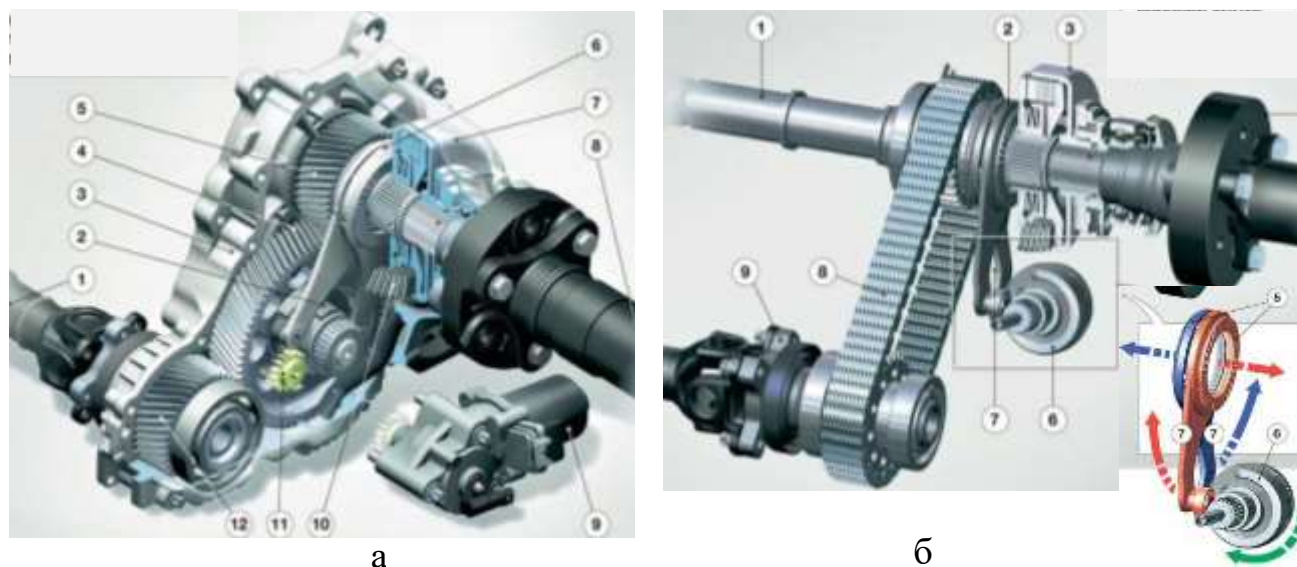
Конструкції роздаткової коробки xDrive:
